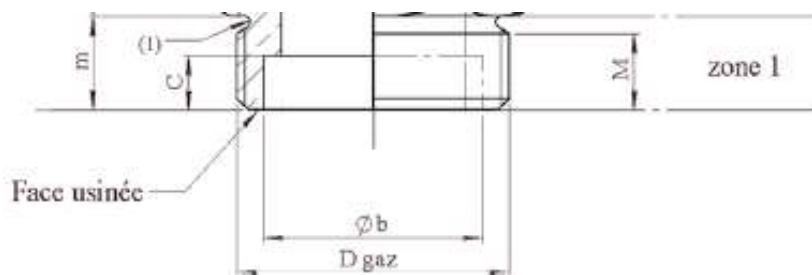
Zone 1 du mamelon d'adaptation à l'installation existante
